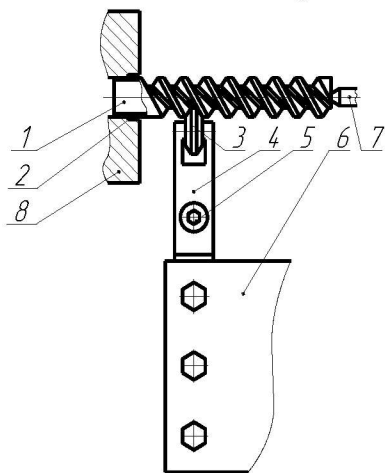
Схема обкочування гвинтових канавок на трубі: 1 – оправка з гвинтоподібним профілем, 2 – деталь, 3 – ролик, 4 – корпус, 5 – пружинний пакет, 6 – різцетримач, 7 – центр, 8 – трьохкулачковий патрон
